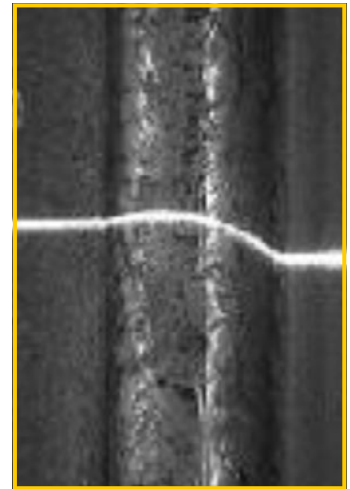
image du joint soudé par laser et de la ligne laser projetée.
